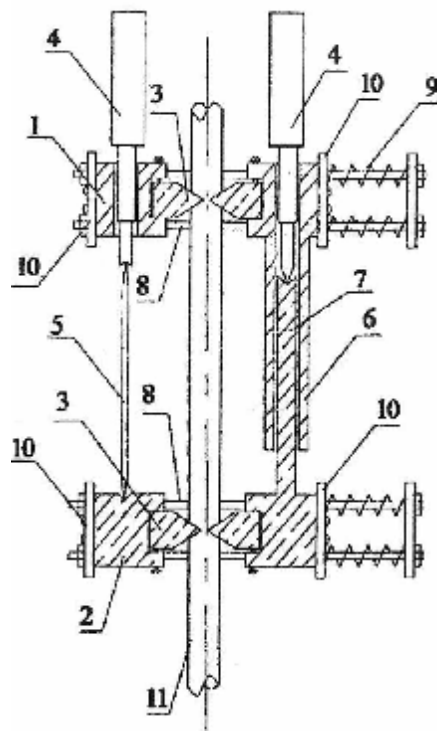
Разработана конструкция приспособления (устройства) для измерения продольных деформаций изделий при их испытании на растяжение, отличающееся особенностями конструктивного расположения элементов
